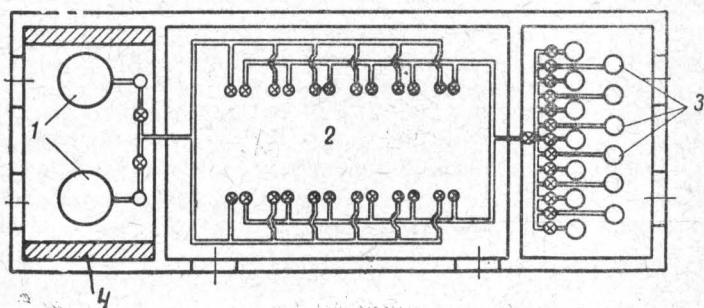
Схема расположения помещений сварочной мастерской при наличии стационарно установленных генераторов
